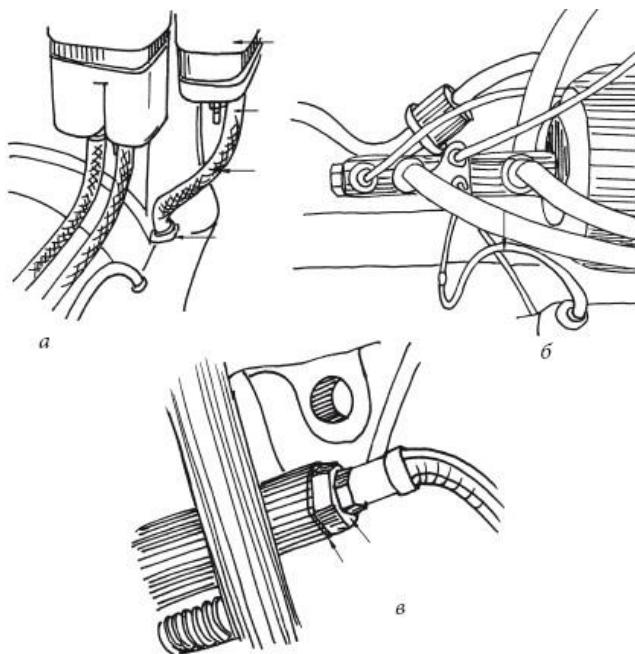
Основные узлы системы сцепления, требующие проверки: а – бачок и штуцер основного цилиндра, б – главный цилиндр, в – место соединения шланга с рабочим цилиндром
